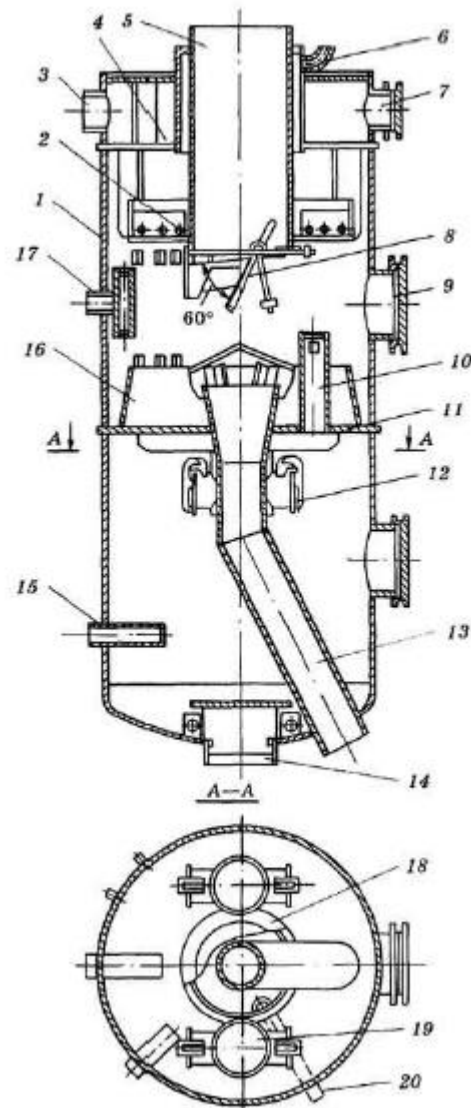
Схема конструкции вертикального смешивающего подогревателя [7]
